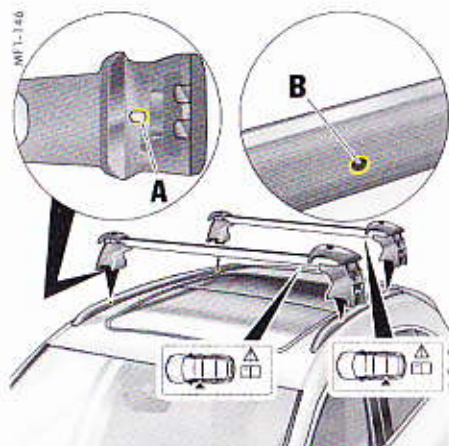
Mise en place et alignement des supports de toit sur les rampes de pavillon
